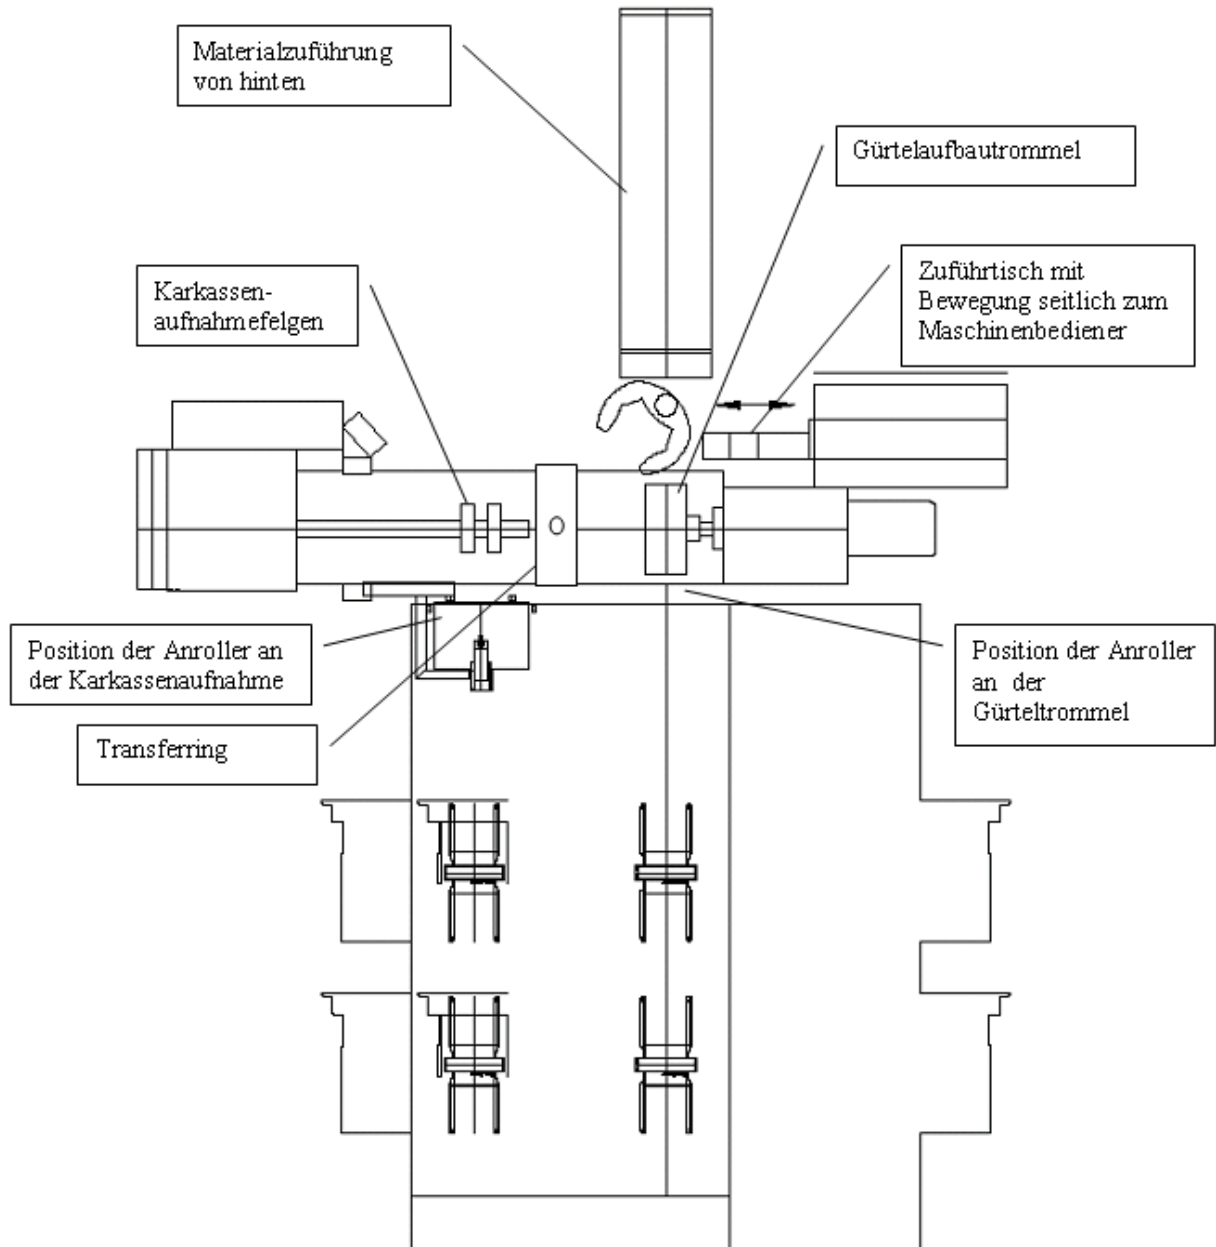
Aufbaumaschine mit Zuführung hinter dem Sichtbereich des Maschinenbediener
